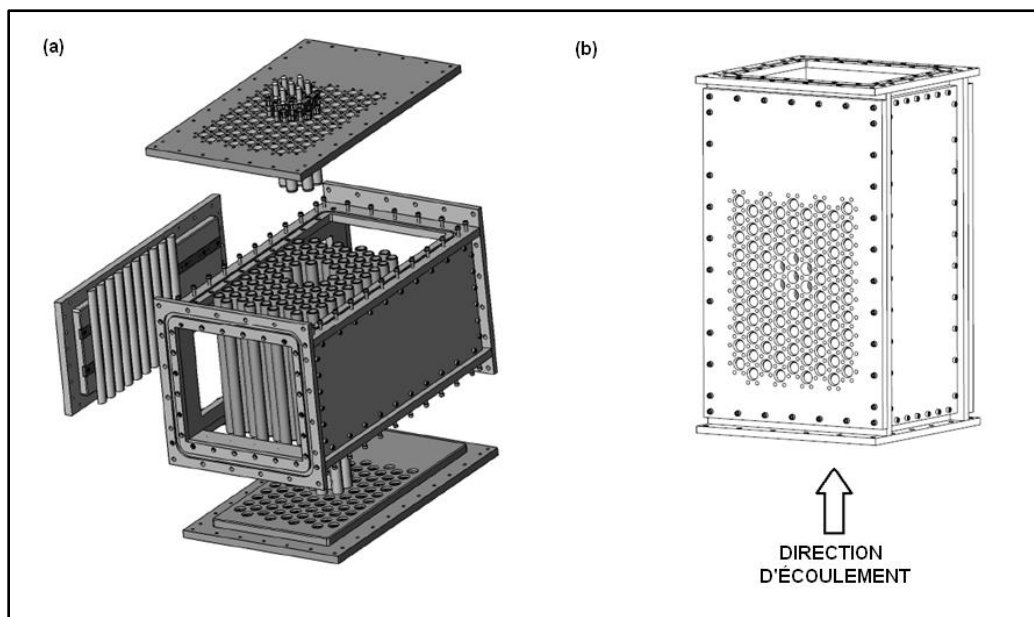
Section d'essai. (a) vue de la section éclatée avec tubes et tubes instrumentés. (b) section assemblée avec direction d'écoulement.
